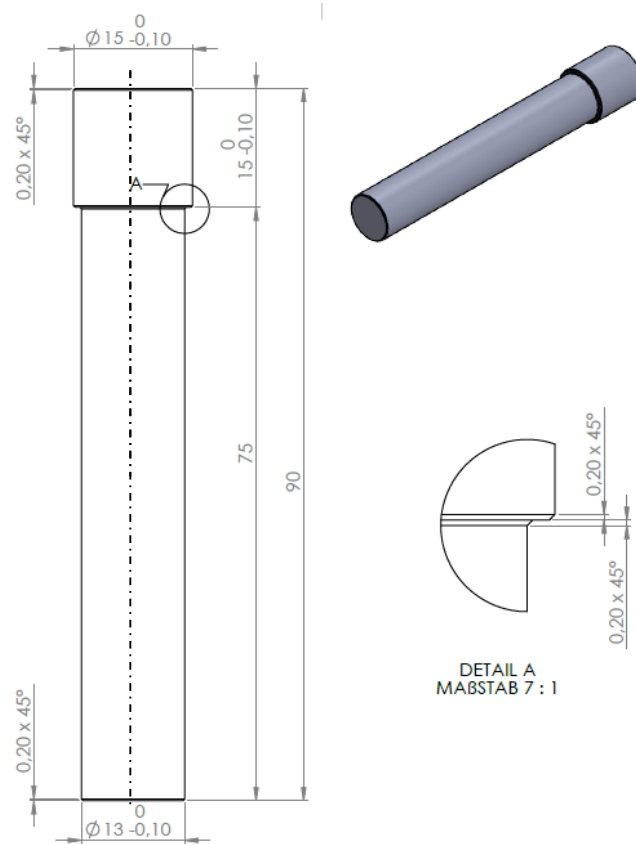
Technische Zeichnung der Probe für das Verjüngen.
